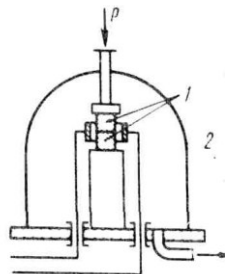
Установка для диффузионной сварки: 1 — свариваемые заготовки; 2 — вакуумная камера
